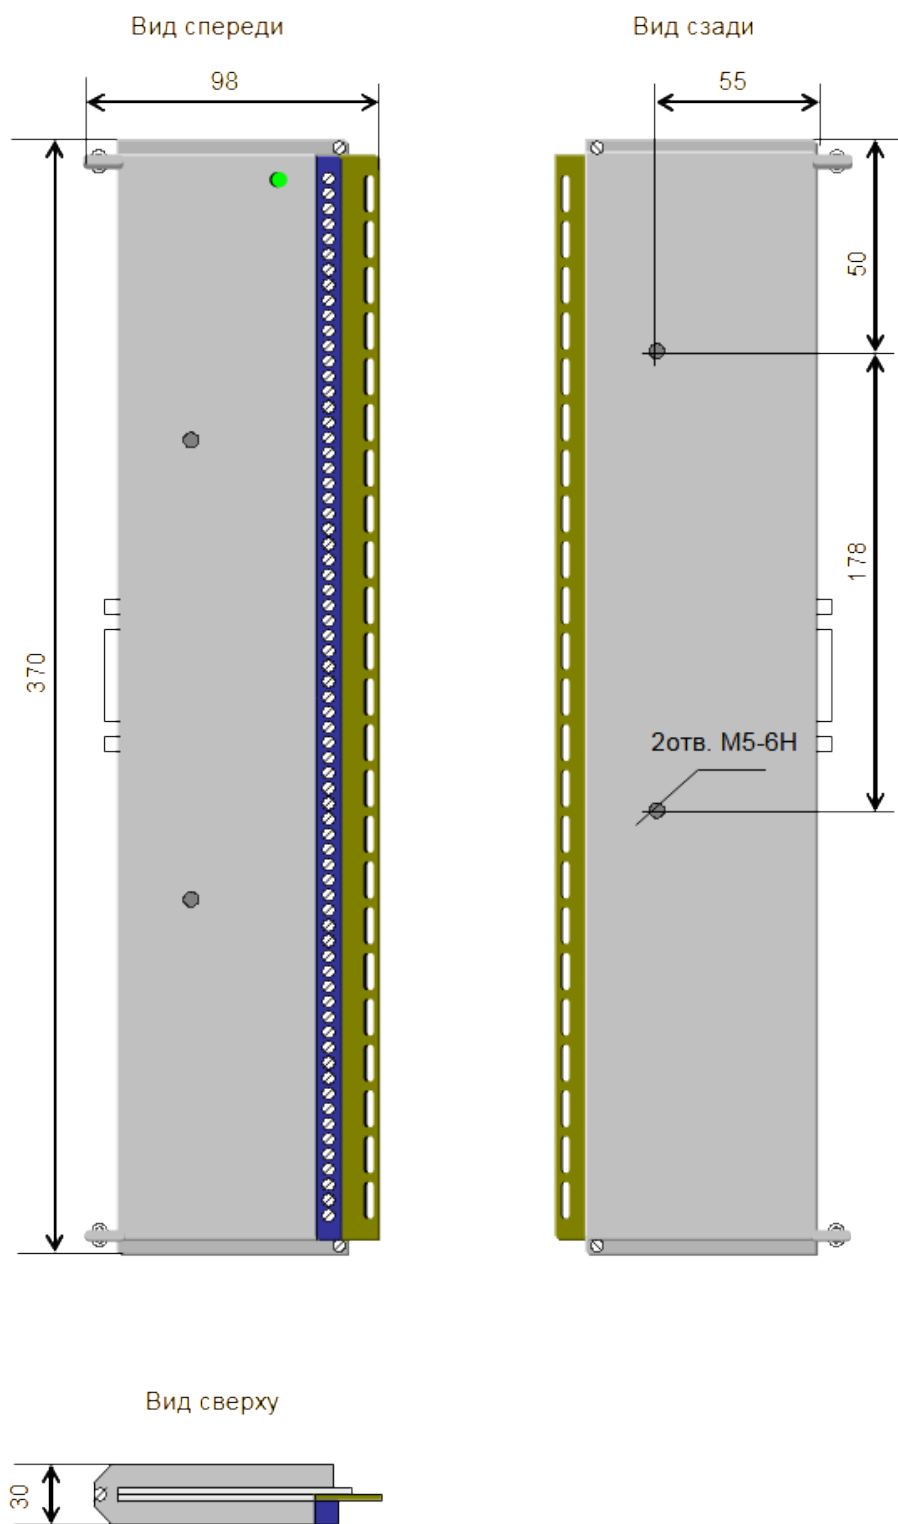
Габаритные и установочные размеры блока сбора дискретных сигналов БКД-64 (артикул СВЕ.01.3108)
